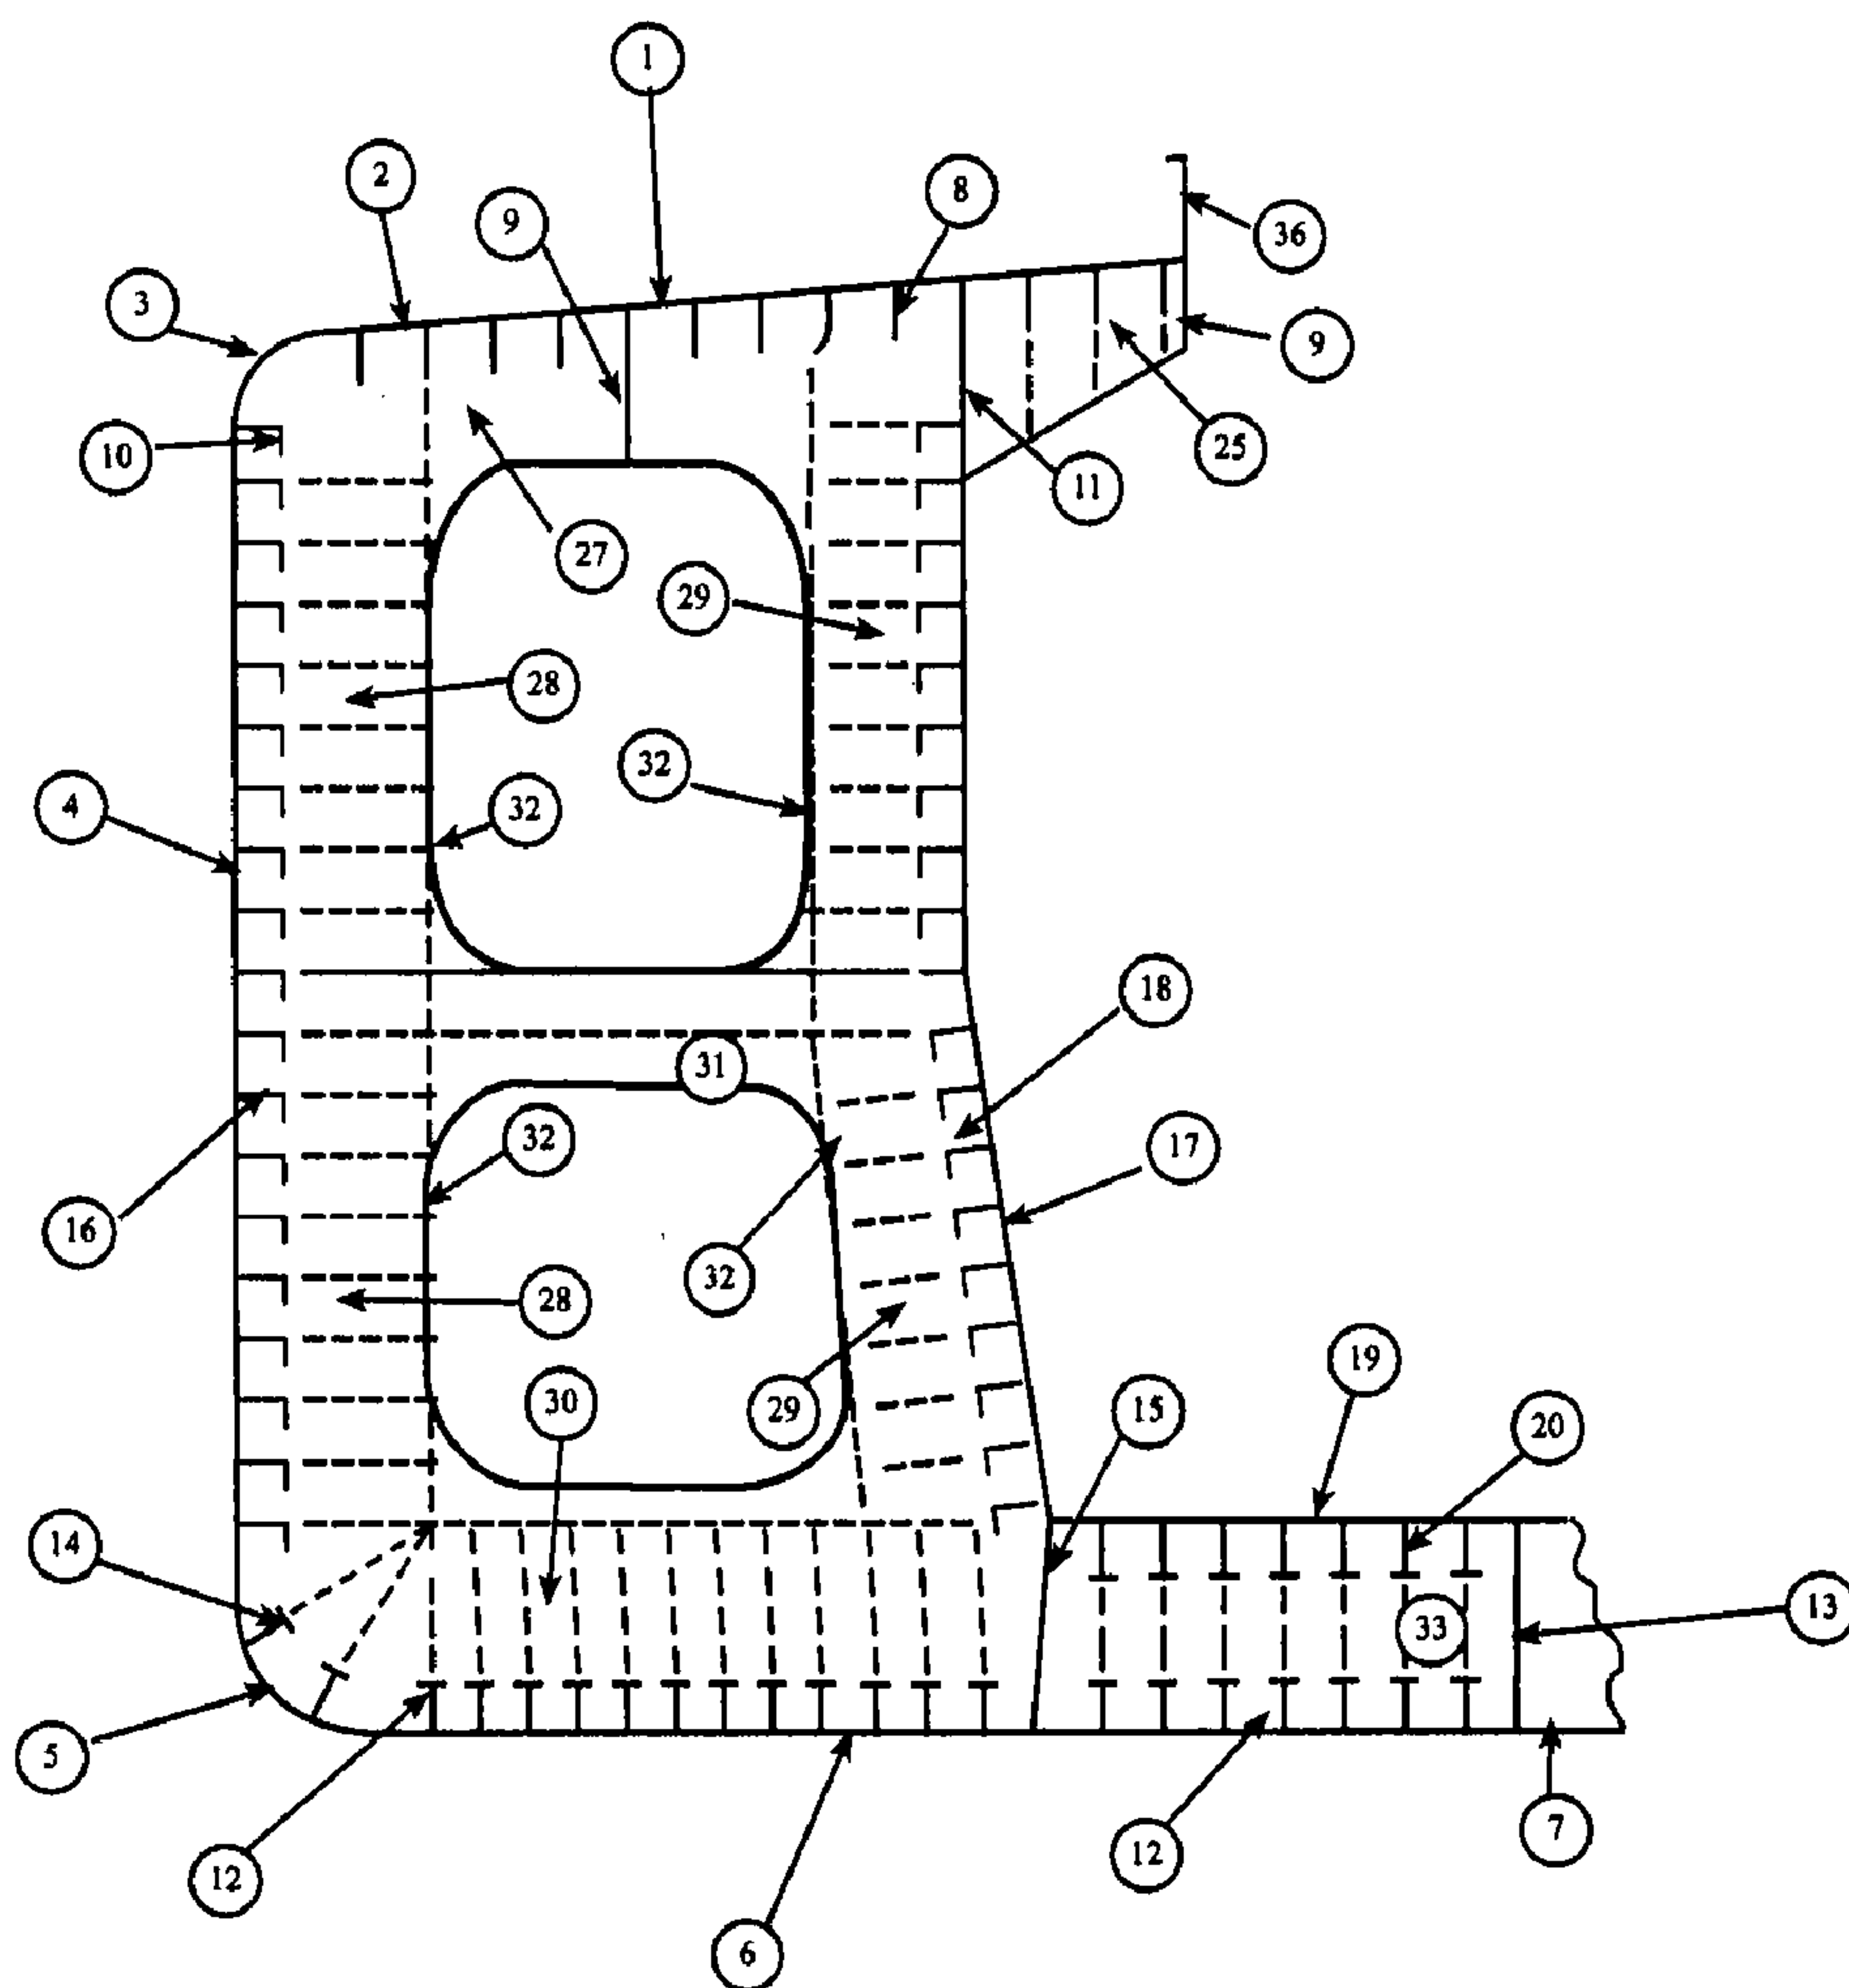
Типичное сечение корпуса нефтерудовоза с обозначением элементов корпусных конструкций:
